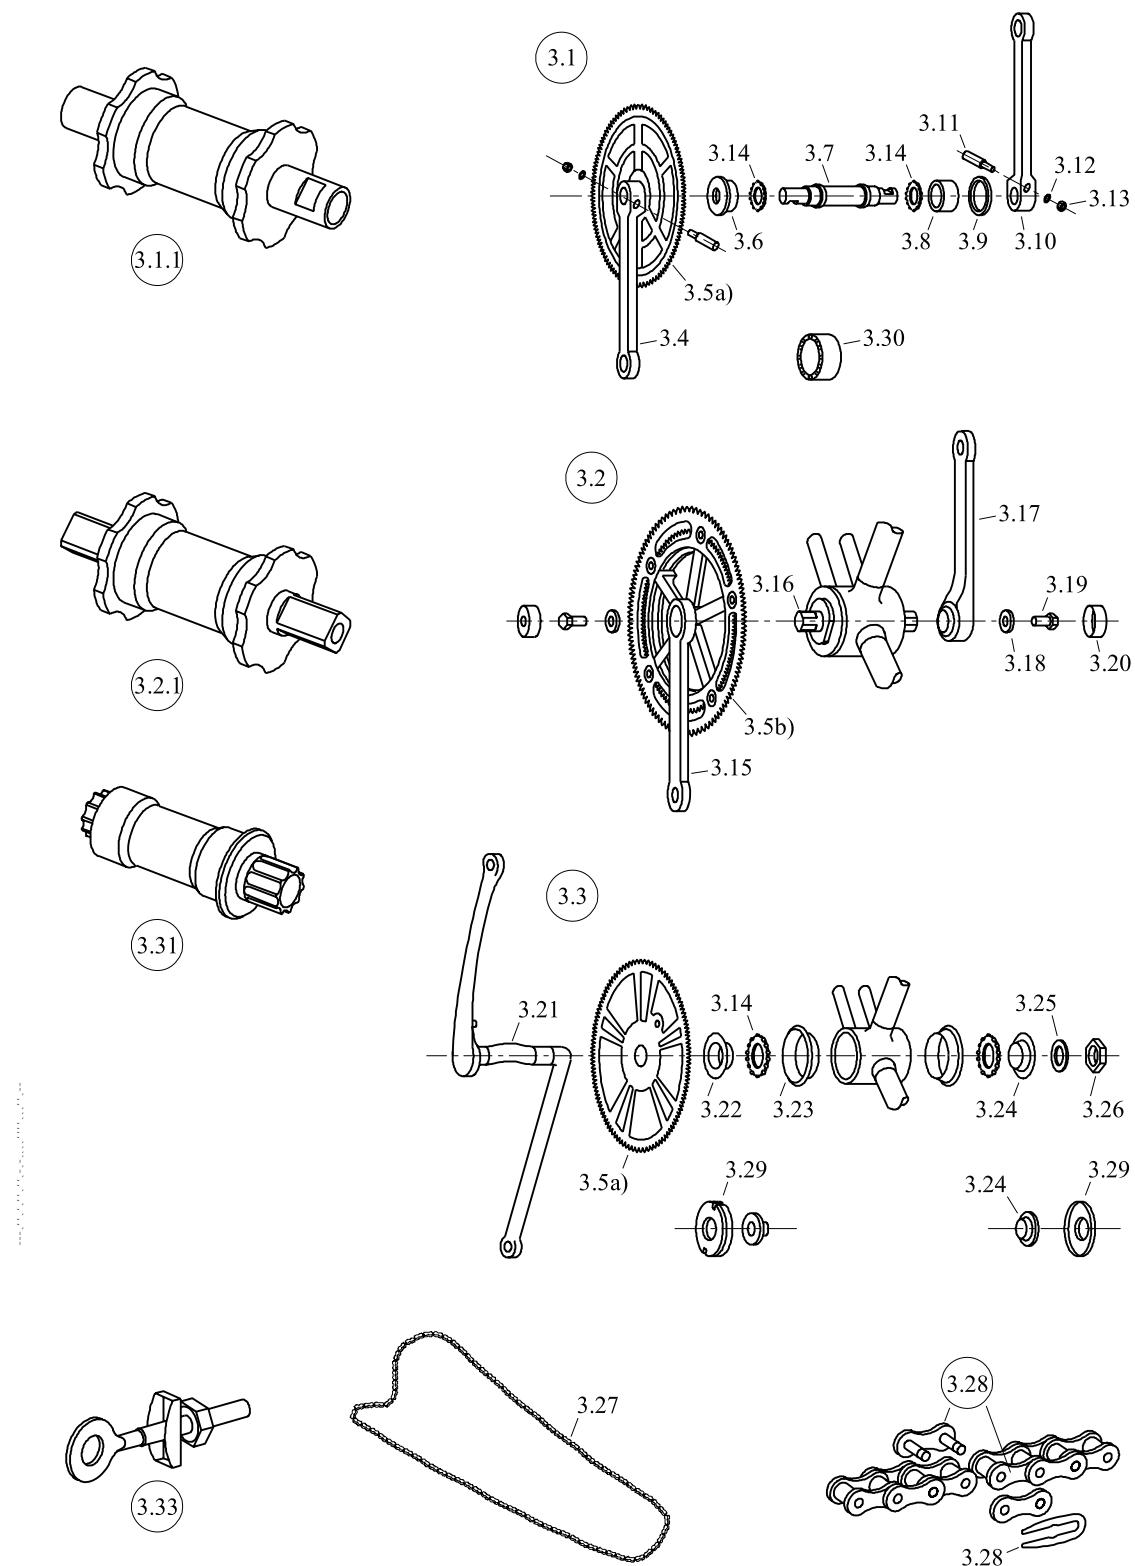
Ensemble boîtier de pédales / Bottom bracket assembly / Tretlager und Antriebskomponenten / Gruppo movimento centrale /Trapas lagerschaal samenscholing
